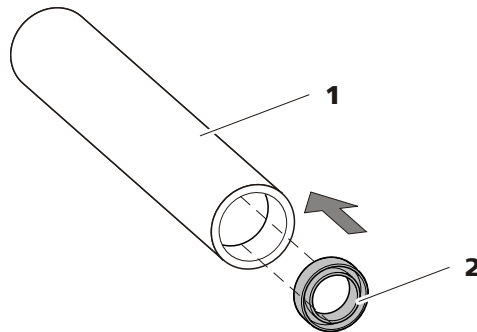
Kolbendichtung in Werkzeug einsetzen
